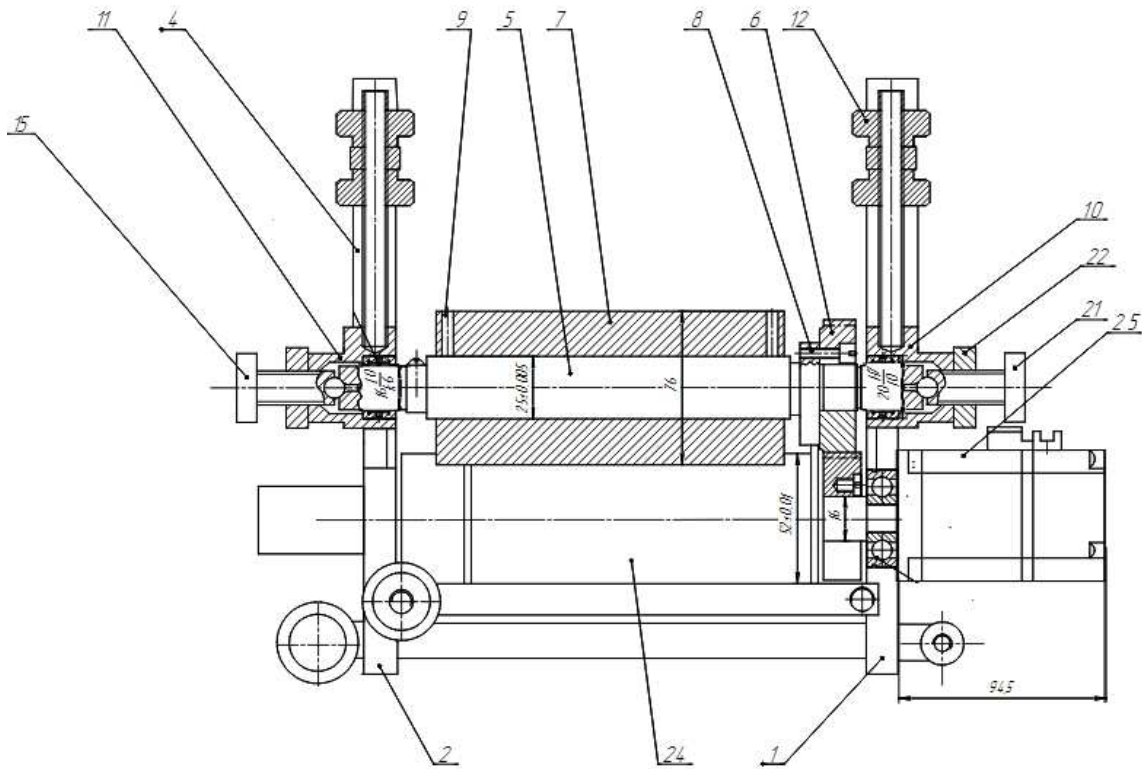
Печатная секция: 1, 2 – плита; 3 – нижняя направляющая; 4 – верхняя направляющая; 5 – ось; 6 – шестерня; 7 – формный цилиндр; 8, 14 – крепежный винт; 9, 18 – винт; 10, 11 – ползуны; 12 – гайка; 13 – планка; 15 – анилокс; 16 – щеки; 17 – собачка; 19, 20 – гайки; 21 – винт приводки; 22 – контргайка; 23, 24 – рамка; 25 – шаговый двигатель
